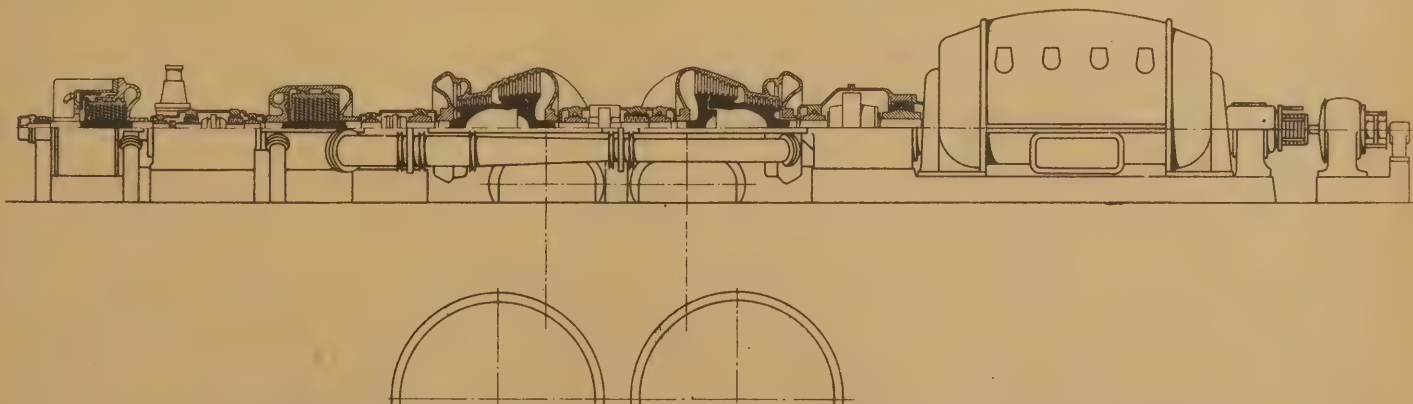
Vierfach-Expansions-Turbine mit geteiltem Niederdruckzylinder. 16000 kW, 8000 Uml./min, 30 at Überdr. 400°C.
